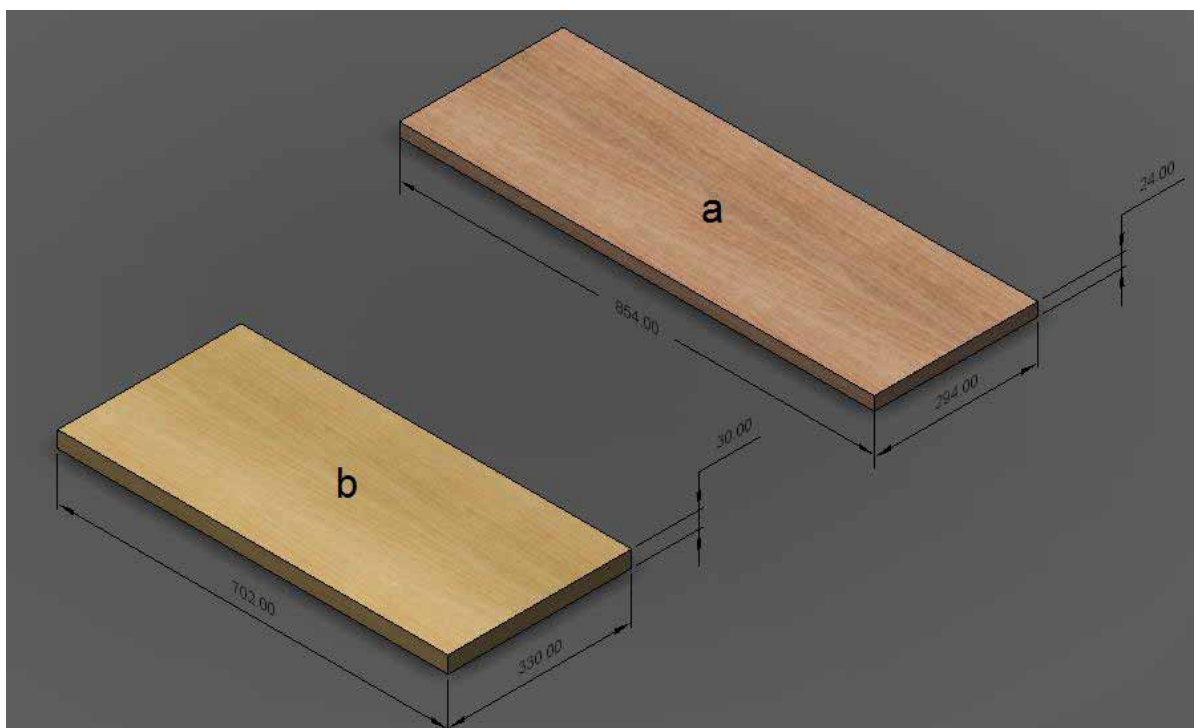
Pré-corpos de prova para Usinagem: a) Eucalipto e b) Pinus.
